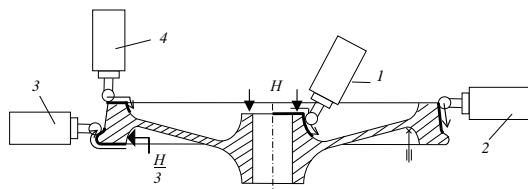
Схема обробки колеса на верстатах моделей 1Б502, 1Б502С, 1Б502
